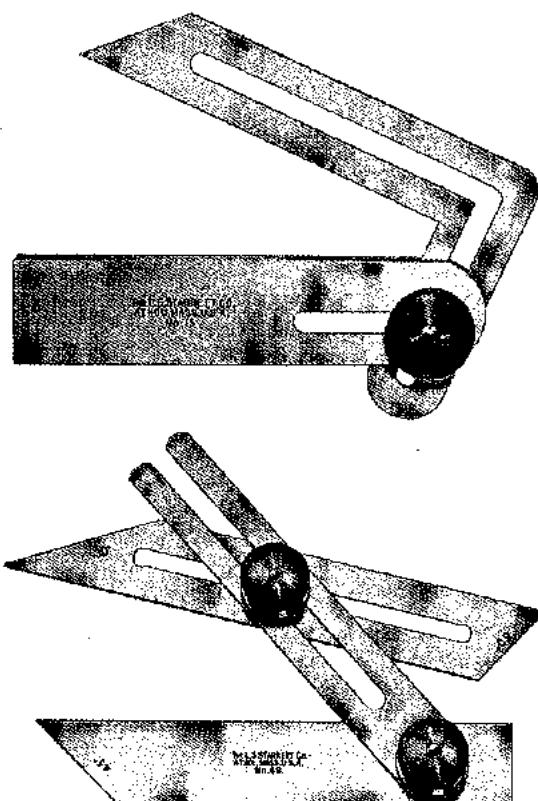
(A) Comprobador de ángulos universal; (B) Comprobador de ángulos combinado (L.S. Starret Co.)
